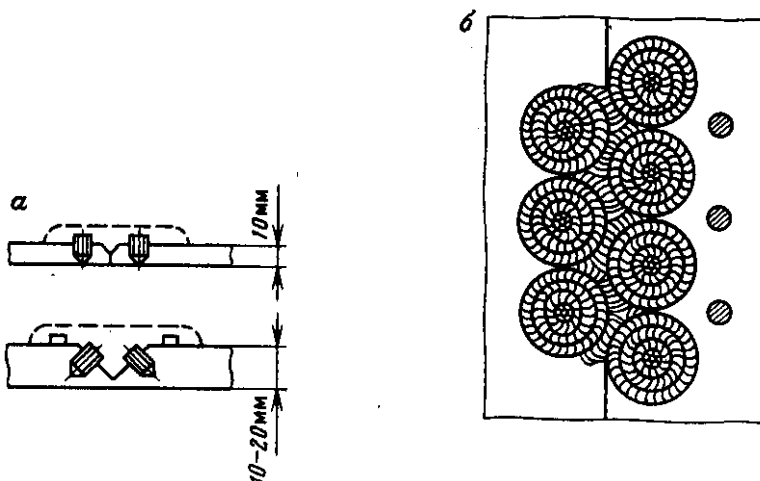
Сварка чугунных деталей с установкой стальных шпилек а – с V – образной подготовкой кромок; б – с обваркой шпилек.
